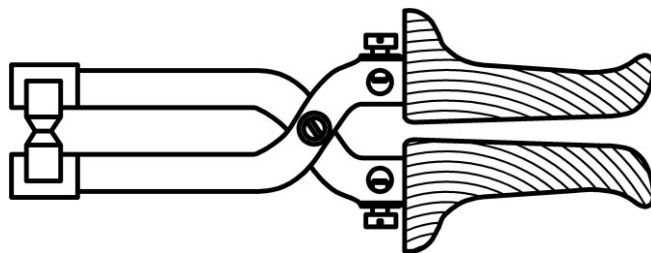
Кліщі Бенардоса для контактеного зварювання
